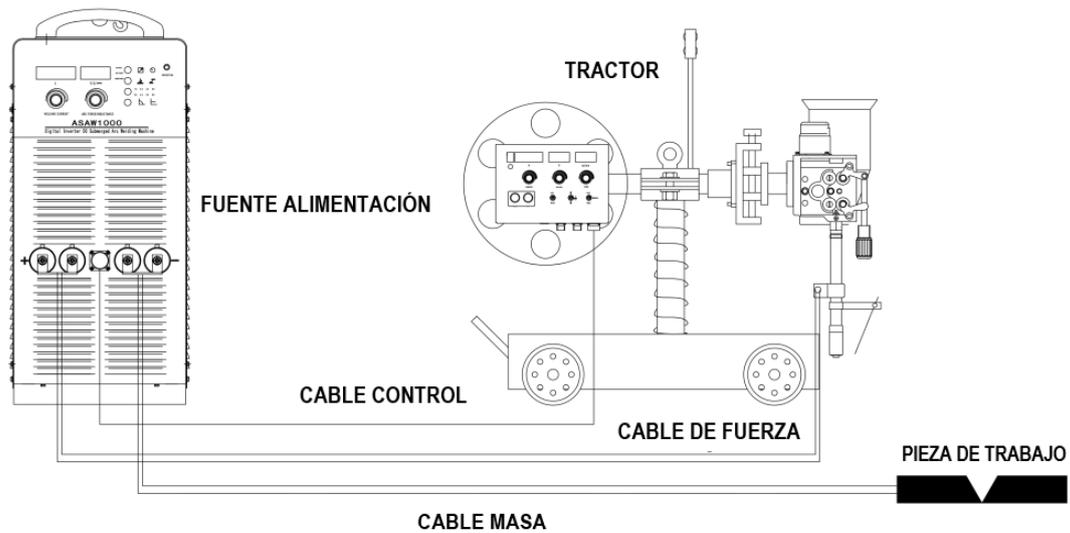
Conexión entre máquina de soldar y tractor
